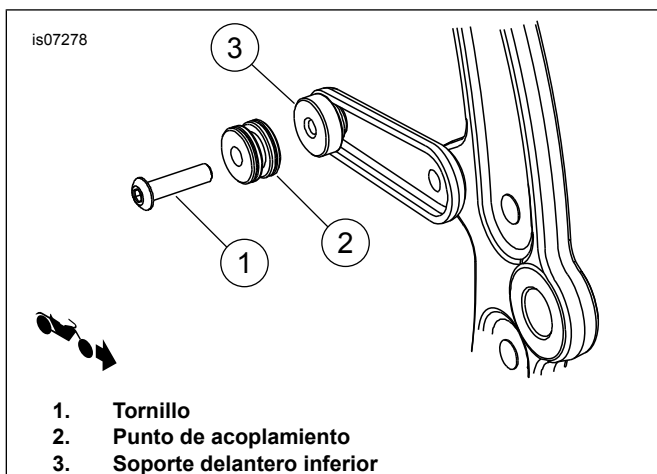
Punto delantero de acoplamiento inferior (sin otros accesorios desmontables)
